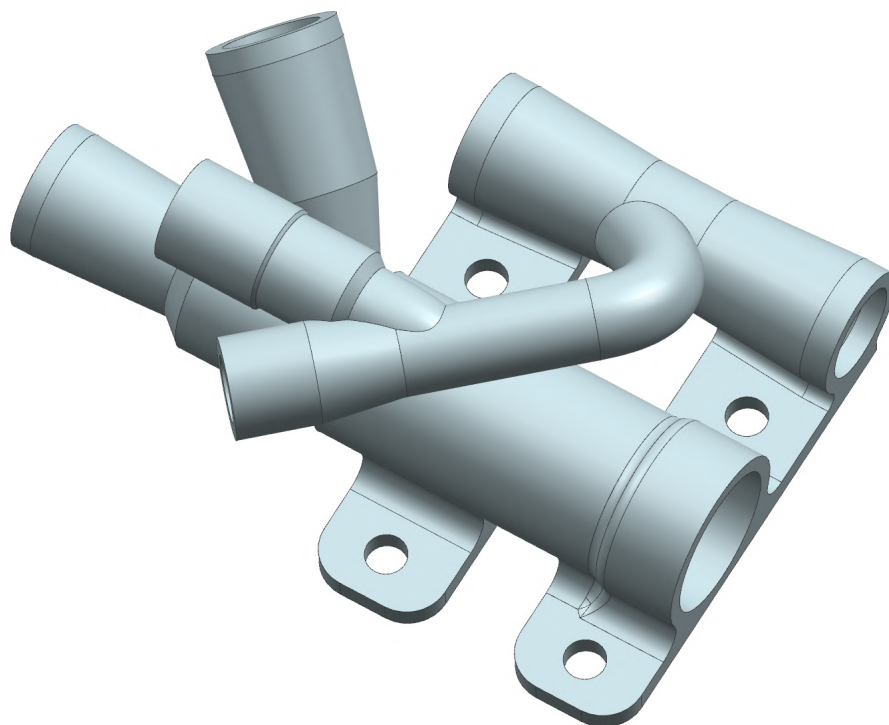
Verze 1 - pohled zepředu zprava shora
